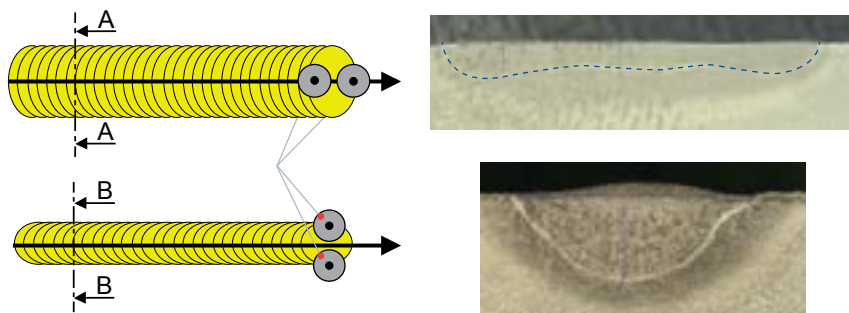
Асимметричная форма дуги и сварочной ванны.
